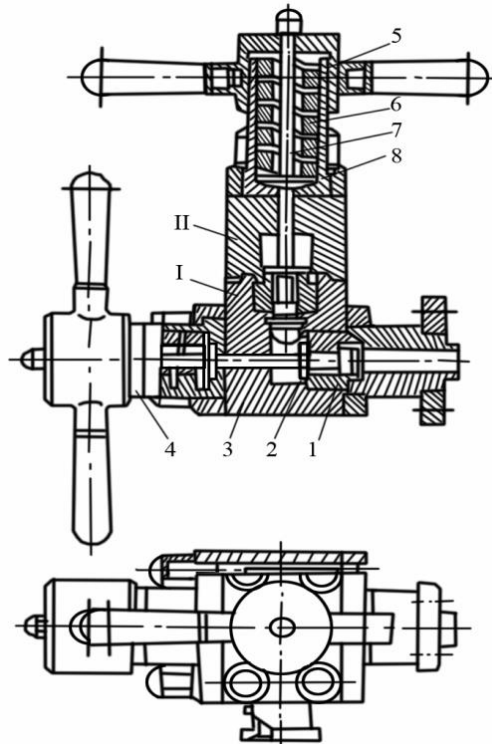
Двохступінчаста гомонізуюча головка I – перша ступінь; II – друга ступінь; 1 – сідло клапана; 2 – клапан; 3 – корпус; 4 – натискний пристрій; 6 – пружина; 7 – шток; 8 – стакан
